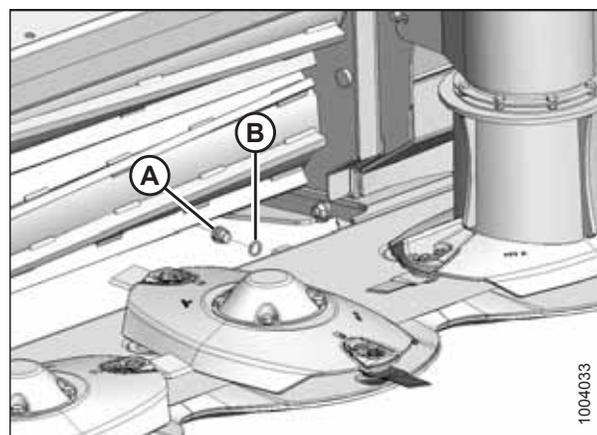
Bouchon d'inspection d'huile de barre de coupe
